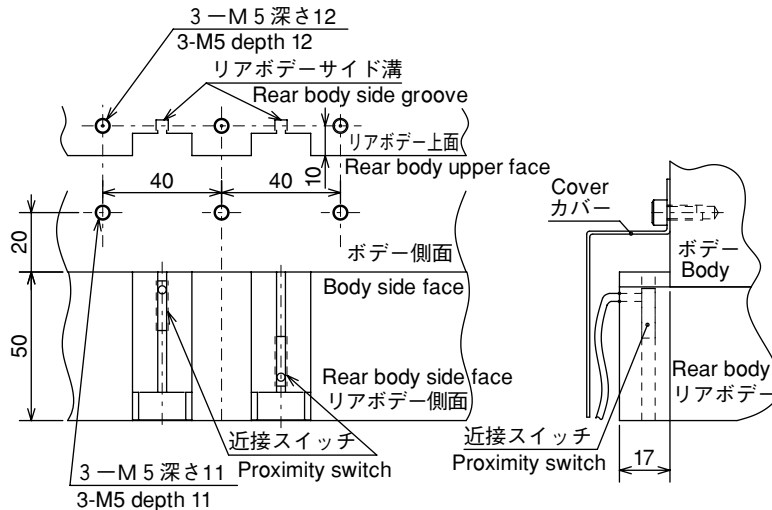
近接スイッチ取付図 Mounting Drawing of Proximity Switch
